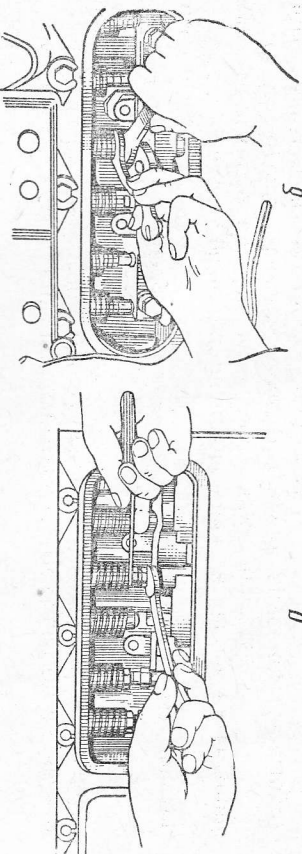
Регулировка зазора между стержнем клапана и толкателем: а — установка зазора; б — закрепление контргайки регулировочного болта толкателя.
